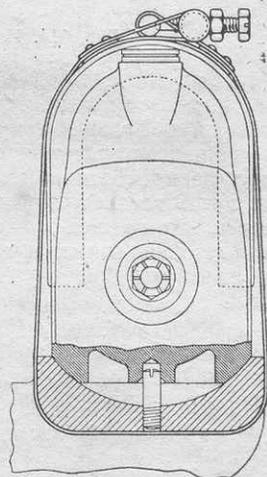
Ленточный хомут для крепления магнето с цилиндрической опорной поверхностью.
